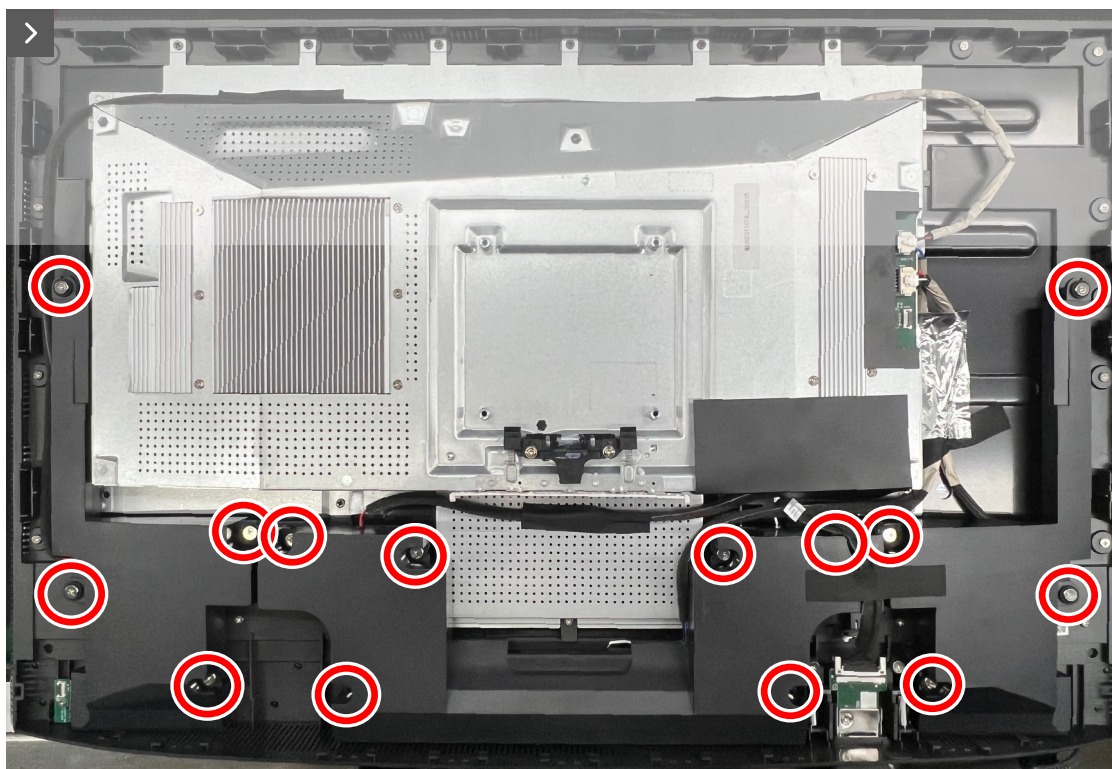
Installazione delle viti e collegamento dei cavi altoparlante
